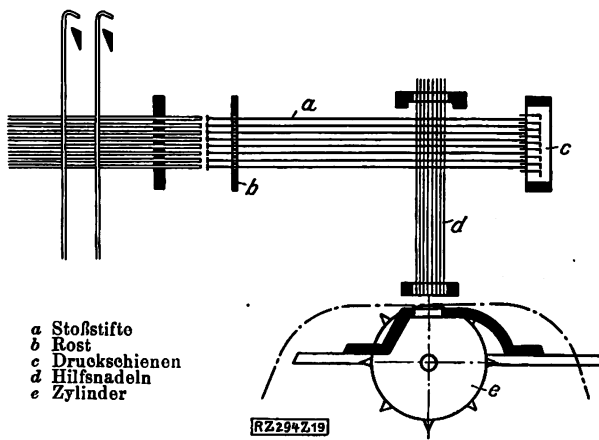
Verdolmaschine der Maschinenfabrik Carl Zangs, A.-G., Krefeld
